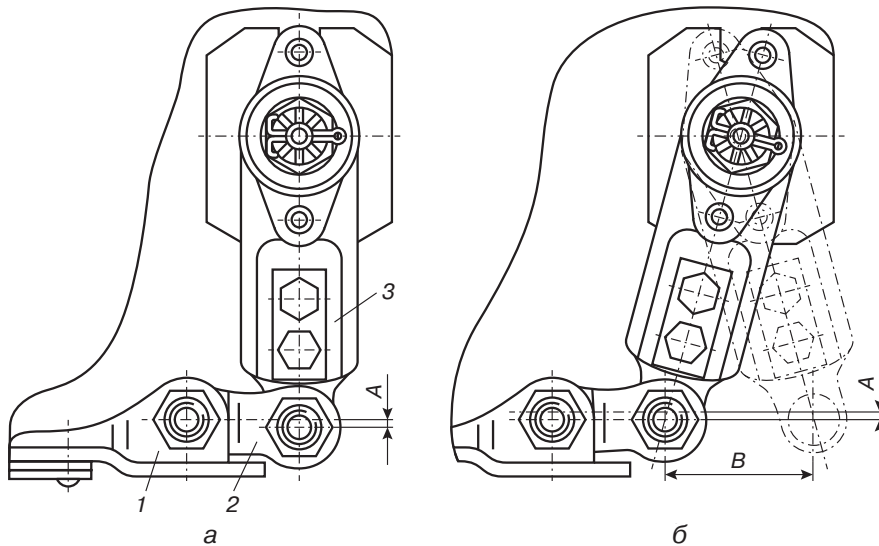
Регулювання з'єднання головок ножа і важеля механізму коливальної шайби: а — важіль у середньому положенні; б — важіль у крайніх положеннях; 1 — головка ножа; 2 — з'єднувальна щічка; 3 — головка важеля; А — зміщення осей головок важеля та ножа ( $A = 2,5-3,0$  мм); В — хід головок важеля і ножа ( $B = 88$  мм)
